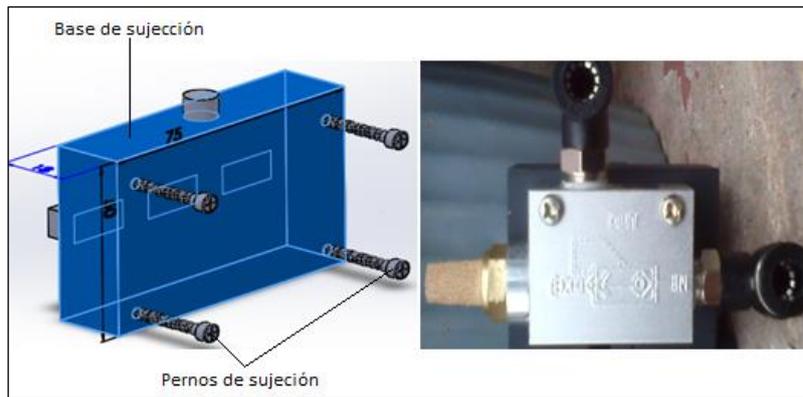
Elementos de fijación y válvula de escape rápido.
